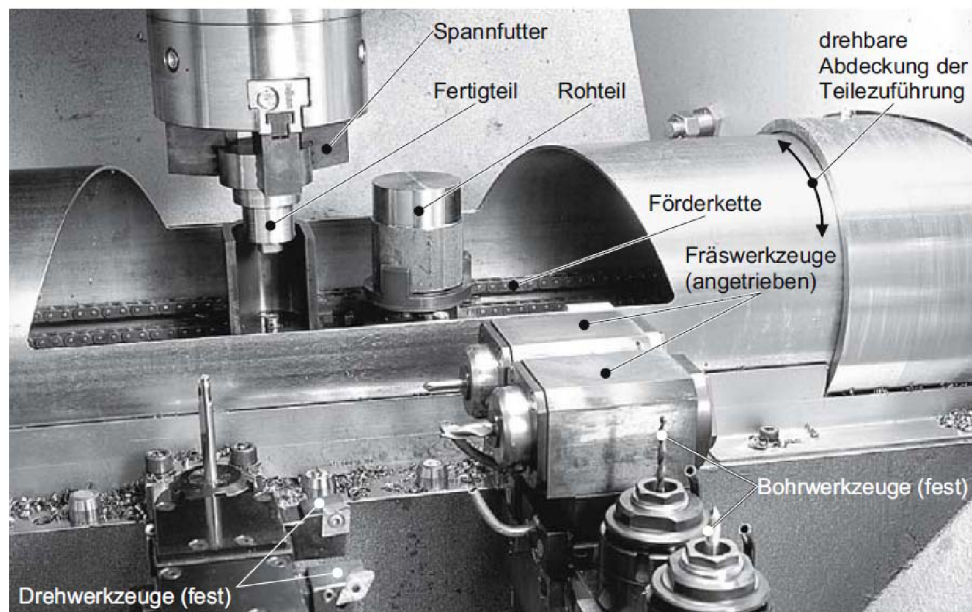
Werkstückwechsel mit Pick-Up-Spindel [8].
